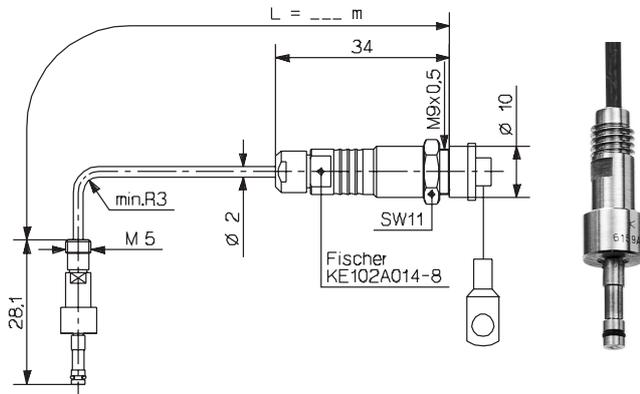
Quarz-Sensor für Werkzeuginnendruck bis 2 000 bar beim Spritzgiessen von Kunststoffen
